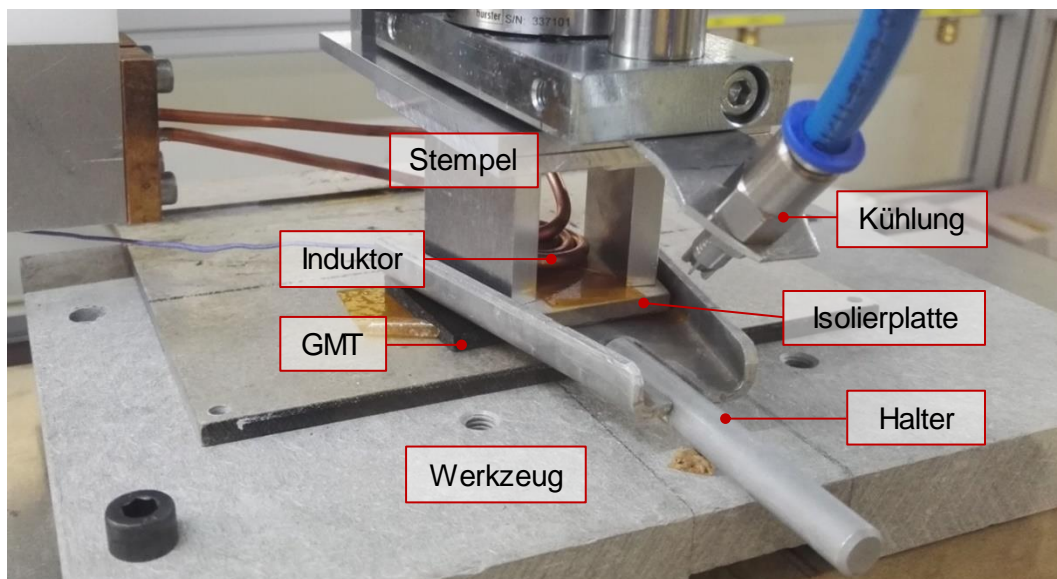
Versuchsaufbau zum weggeregelten Schweißen des Unterbodenblech-Demonstrators
